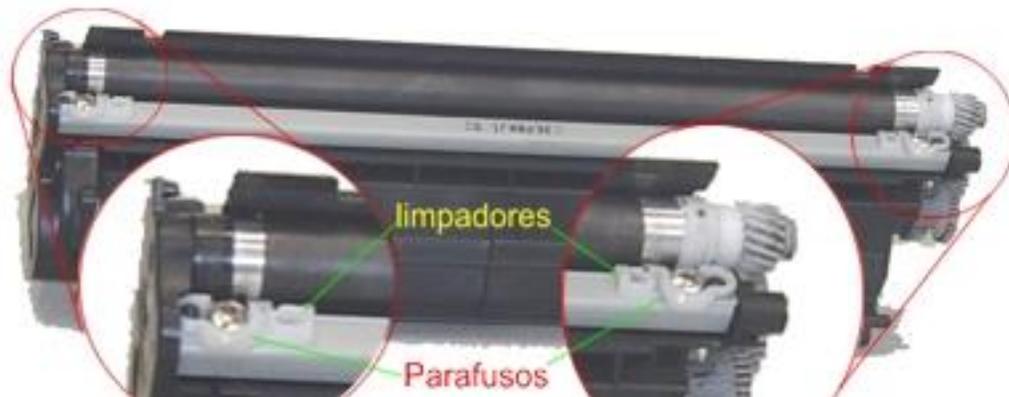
9 - Seção de pó - detalhes da montagem
